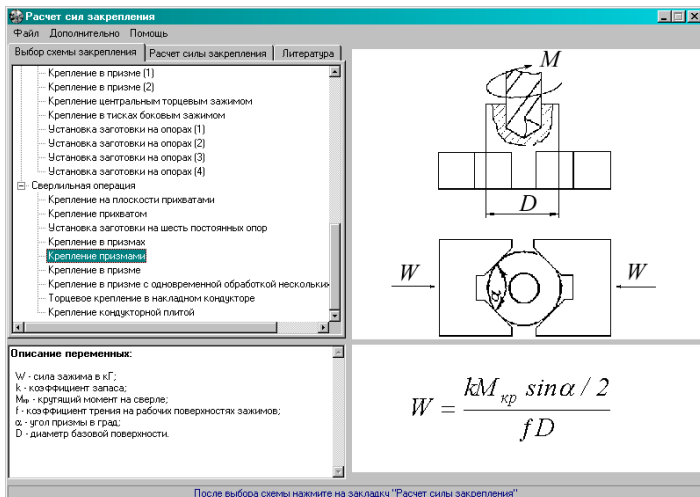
Скріншот вибору закріплення, якщо заготовка закріплена двома призмами
